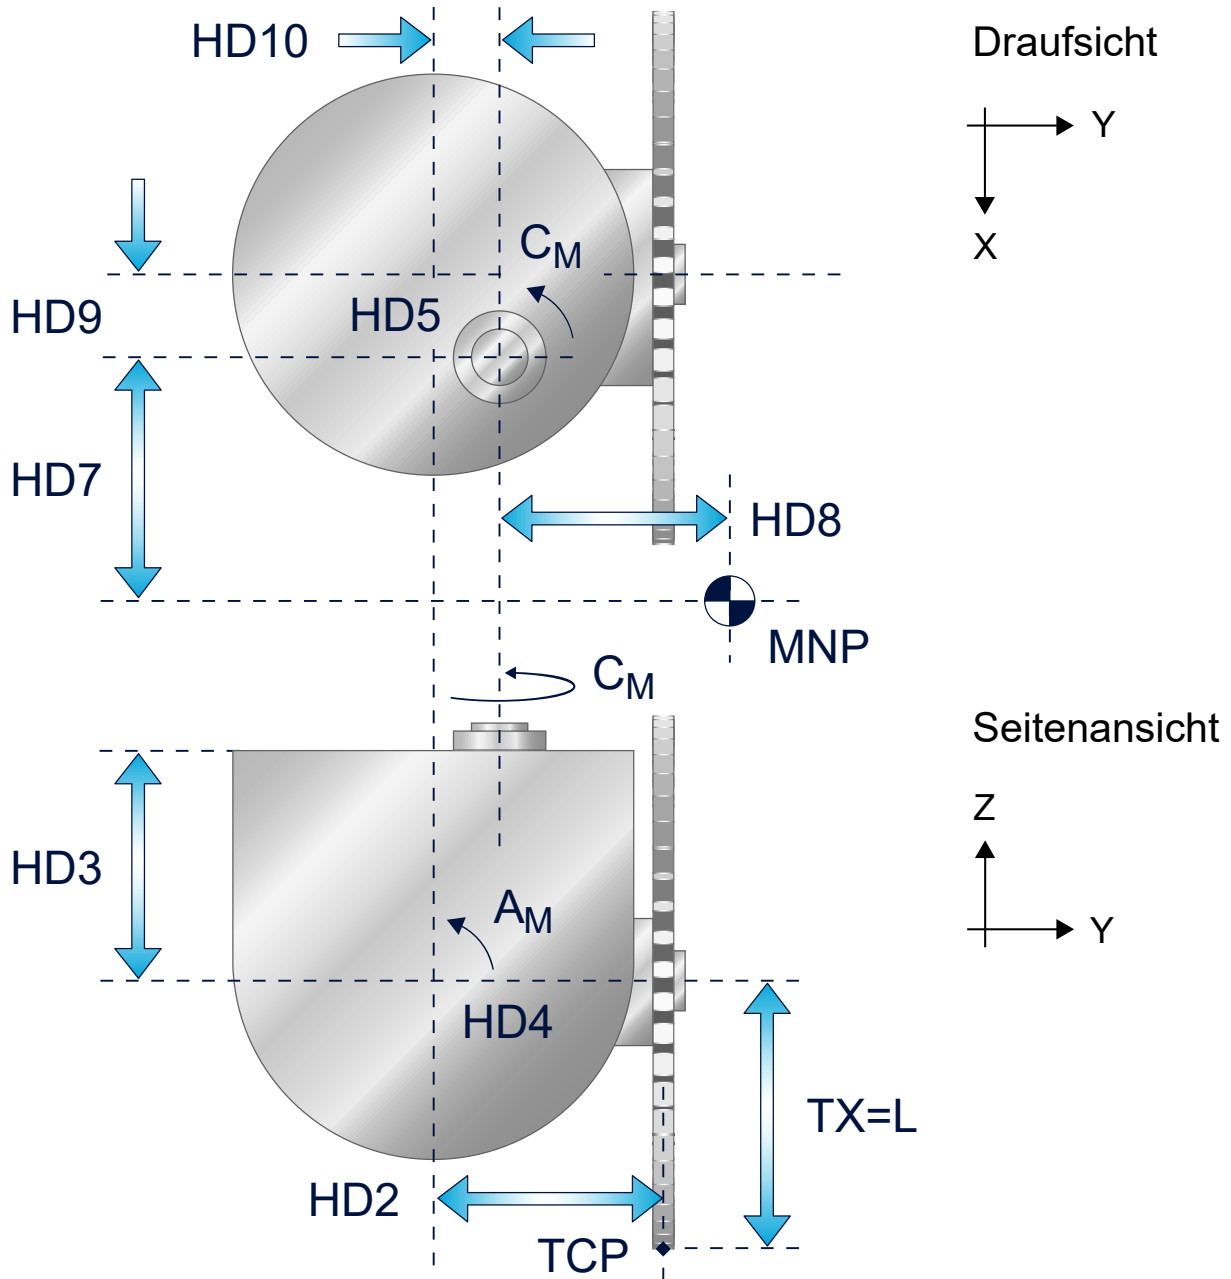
Sägewerkzeug (Ruhestellung mit HD5 = 0, HD4 = +90)
